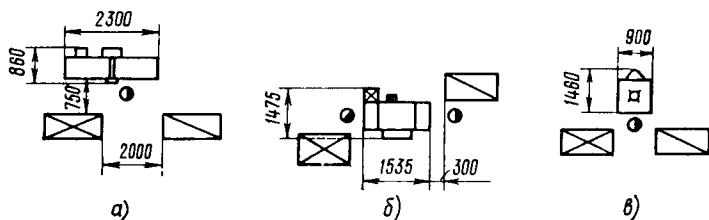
Схема организации рабочих мест у фуговального (а), рейсмусового (б) и фрезерного (в) станков
